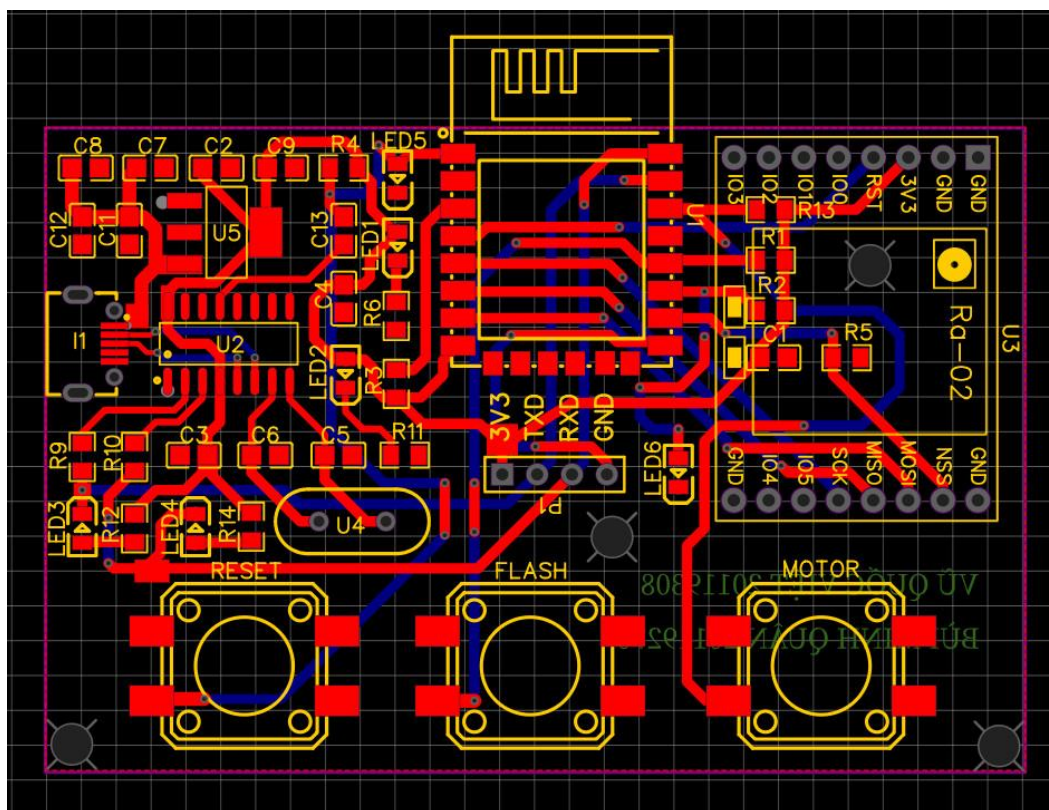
Hình ảnh thực tế PCB bên FARM (chưa có linh kiện)
